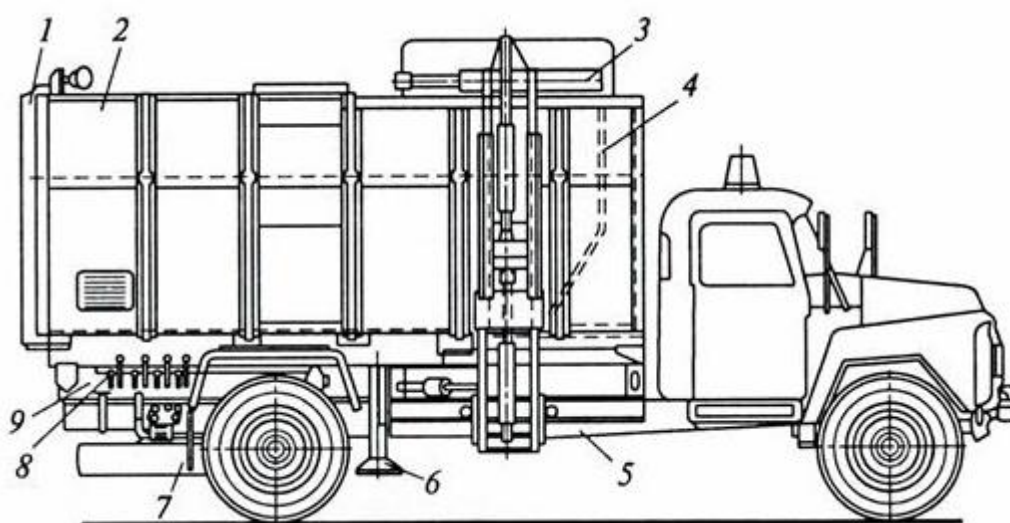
Общий вид кузовного мусоровоза с боковой загрузкой
